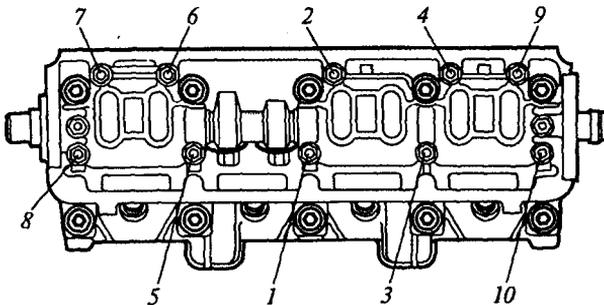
Порядок затягивания гаек крепления корпусов подшипников распределительного вала
